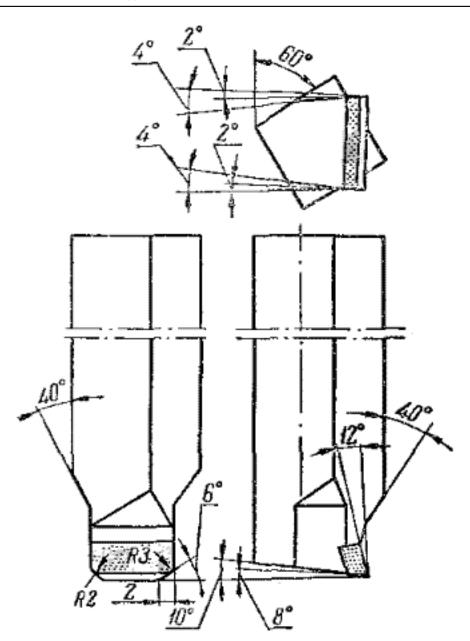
Широкий резец с повернутой режущей кромкой для чистового строга-
